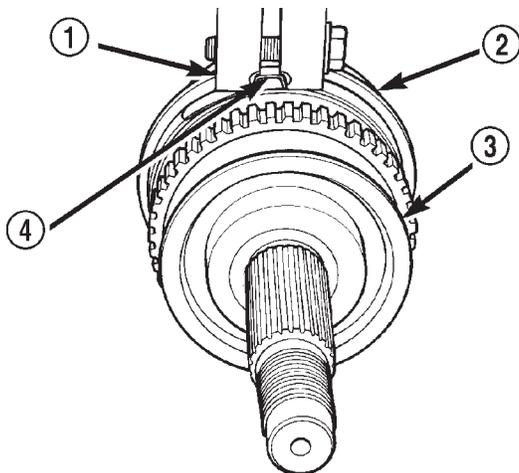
Quetschwerkzeug an der großen Schelle montiert
